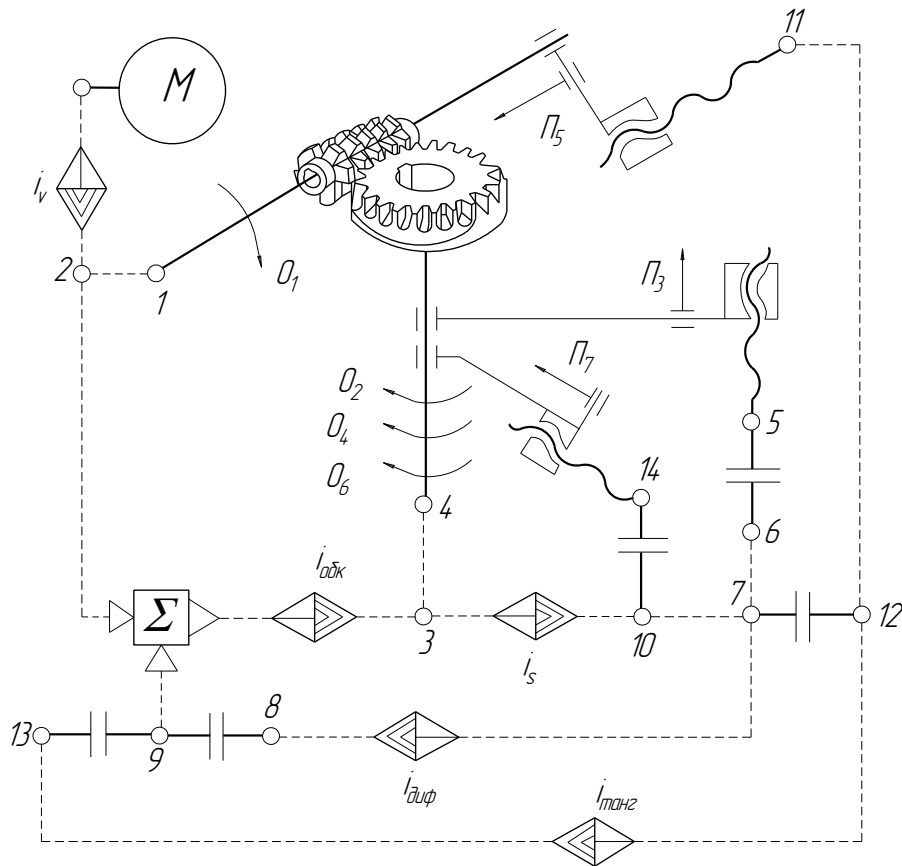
Кінематична структура універсального зубофрезерного верстата
